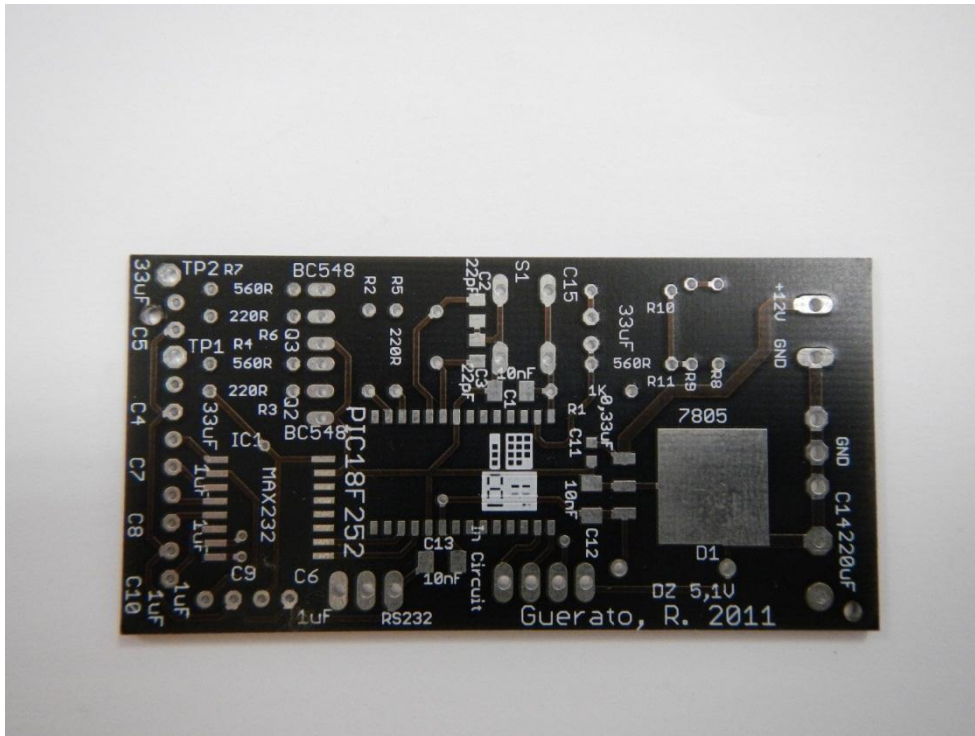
Placa de circuito Impresso pronta para a soldagem dos componentes.
